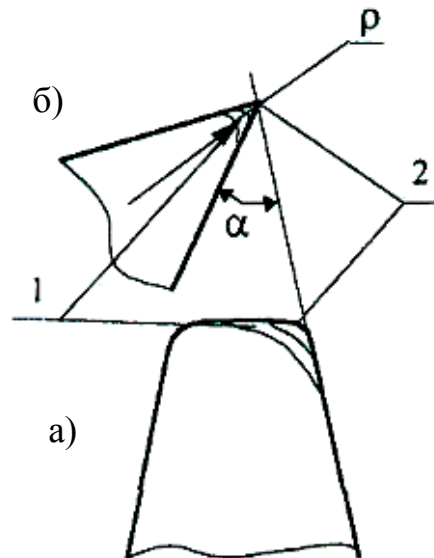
Износ вершин профильной части дисковых зуборезных фрез;
